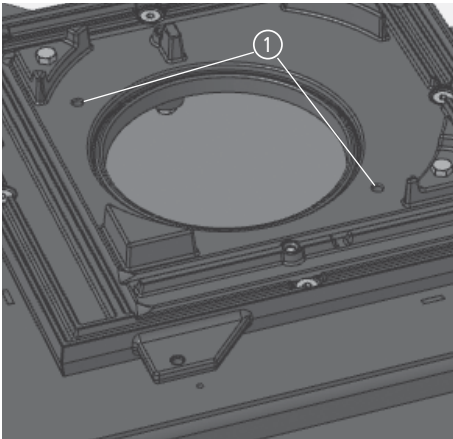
Gewindestifte aus Deckplatte des KALA entfernen
